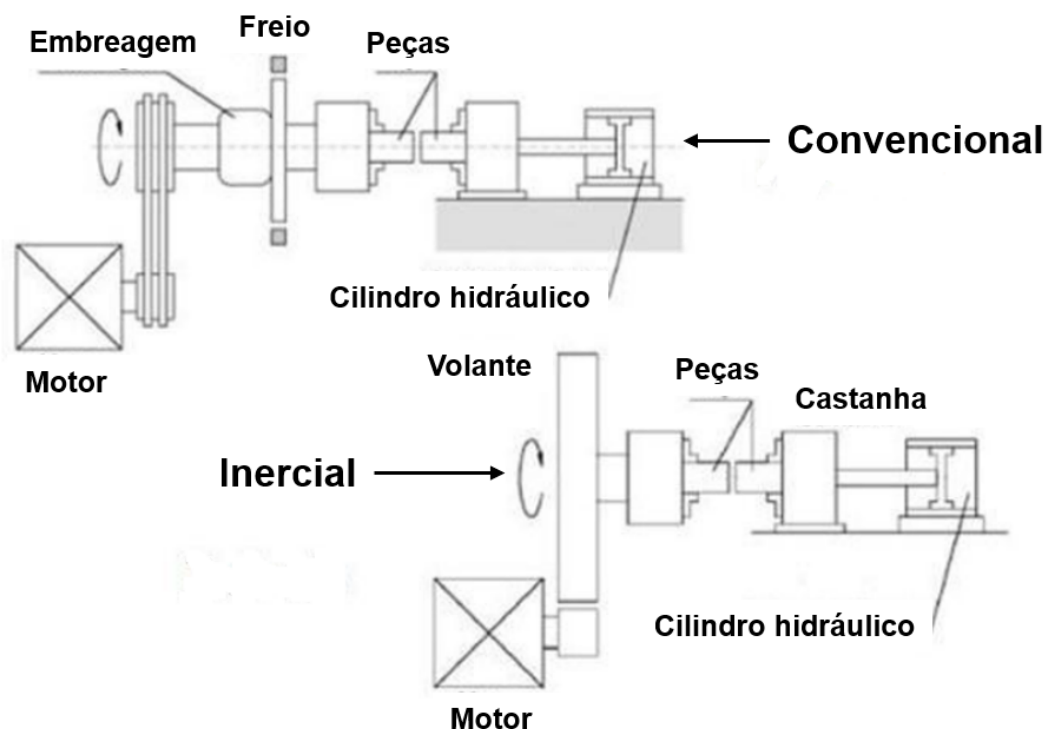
Ilustração do equipamento básico de soldagem convencional e por inércia.
